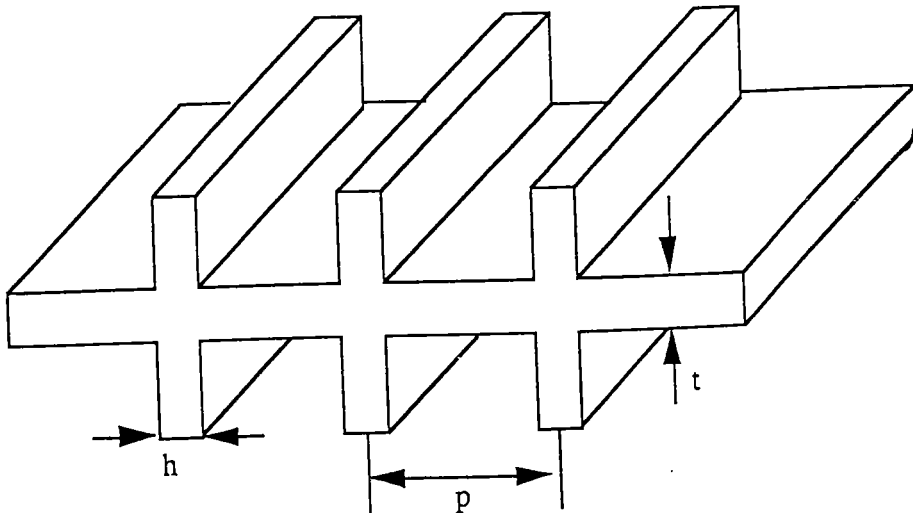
Plaque consolidée par des pièces de renfort équidistantes
